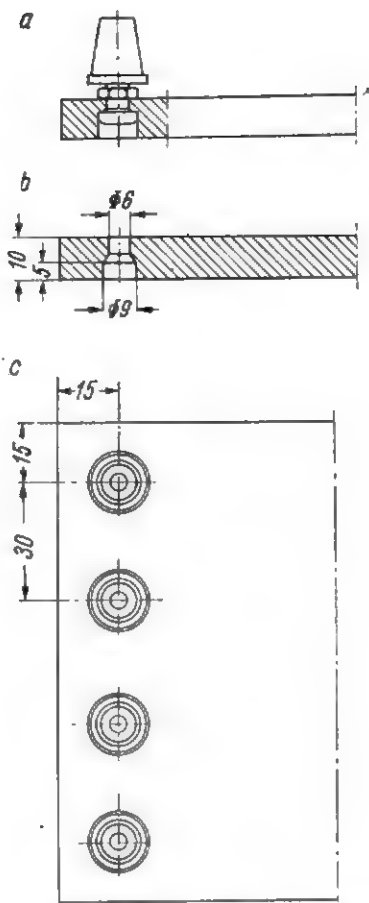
Konstrukcja zacisku do listew łączeniowych
